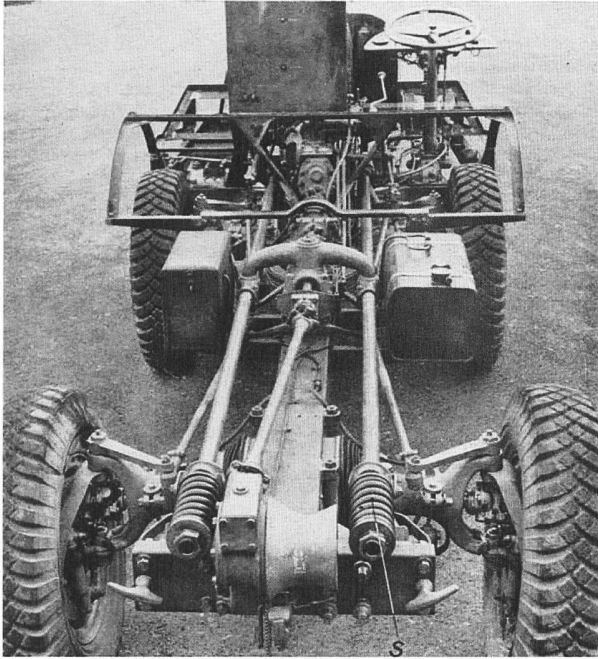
Draufsicht auf das Saurer-Vierradchassis
